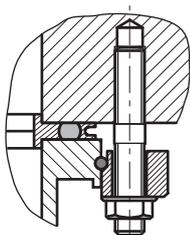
Flanschverbindung ISO-K zu ISO-F, Stiftschraube und Gewindebohrung
